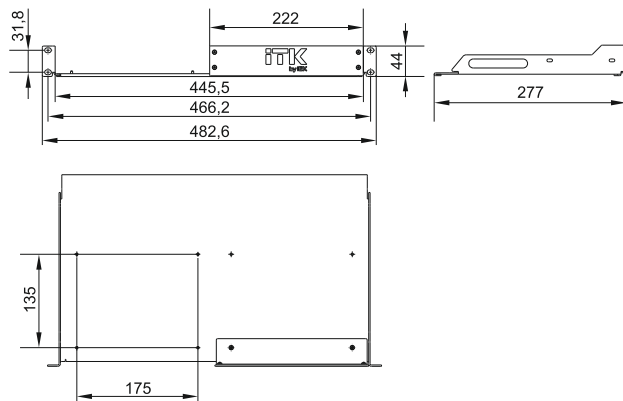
Внешний вид и габаритные размеры изделия / Figure 1 – Appearance and overall dimensions of the product / 1 сурет – Бұйымның сыртқы
